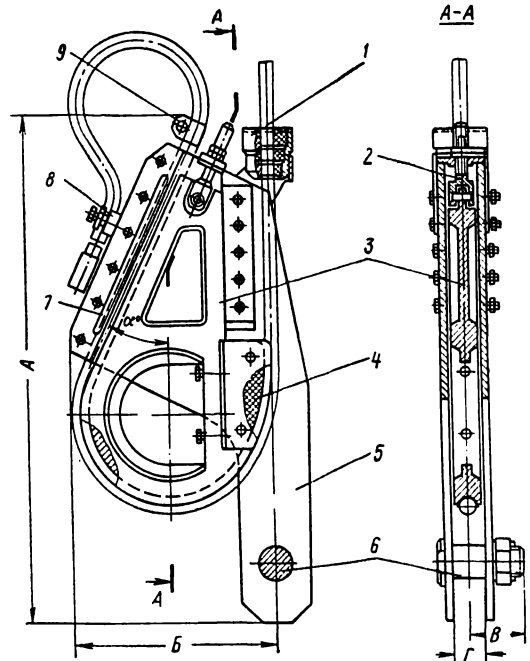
Общий вид коуша клинового безжимкового типа ККБ:
